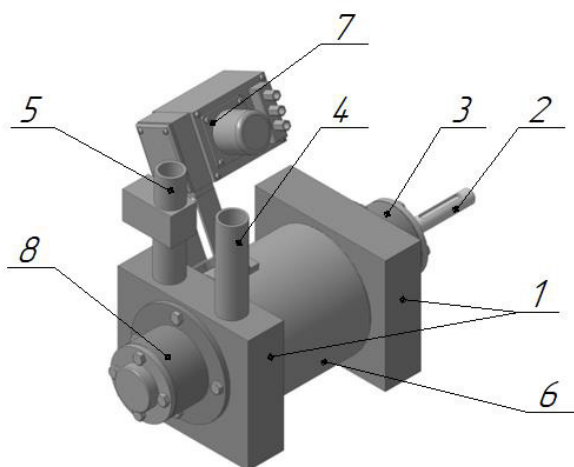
ЖВН с устройством автоматического регулирования нагнетательного окна: 1 – боковые стойки; 2 – вал; 3, 8 – подшипниковые опоры; 4 – впускной патрубков; 5 – выпускной патрубков; 6 – корпус; 7 – нагнетательное устройство
